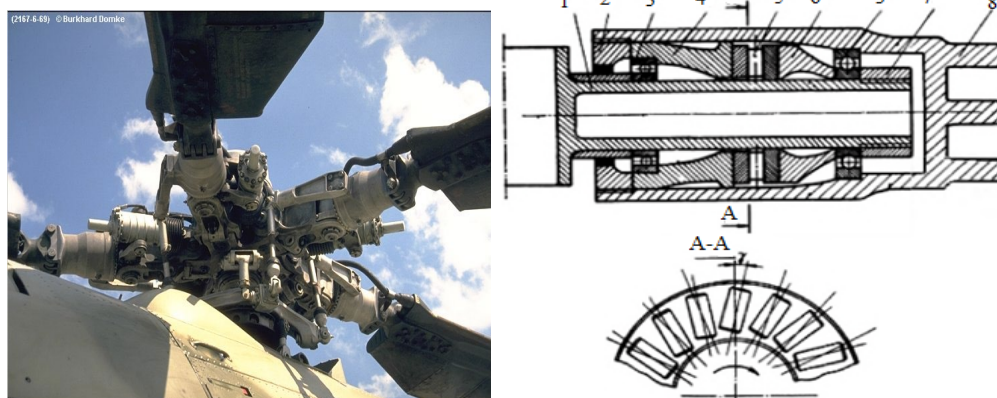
Конструкція осьового шарніра втулки НГ вертольоту Мі-24А: 1 – цапфа, 2 – гайка корпусу осьового шарніра, 3 – радіальний шарикопідшипник, 4 – розпірна втулка, 5 – упорний роликовий підшипник, 6 – упорне кільце, 7 – гайка, 8 – корпус.
